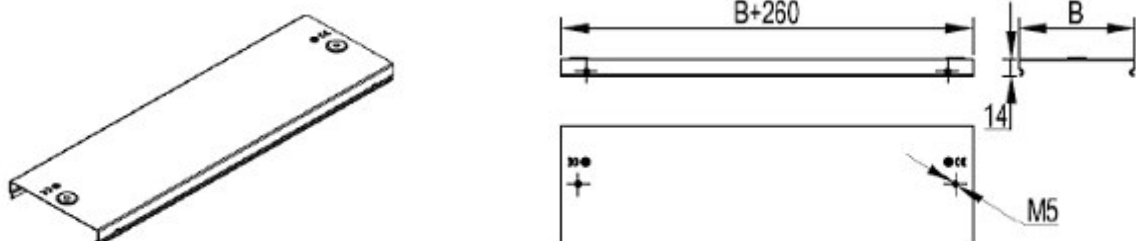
Крышка TDS на ответвитель T-образный вертикальный универсальный
